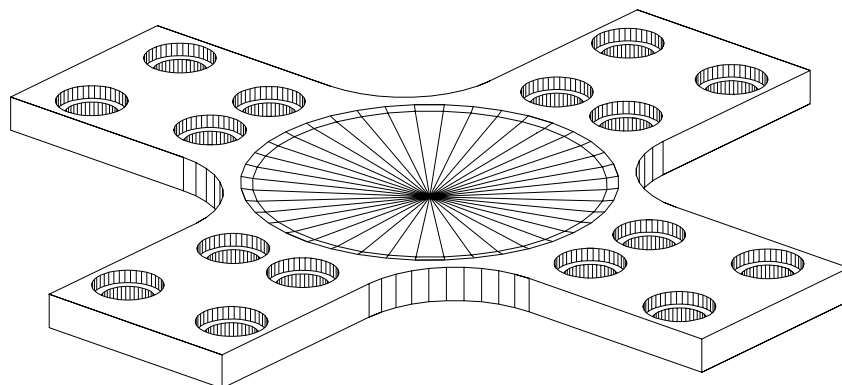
Dessin 3D des éprouvettes cruciformes.
